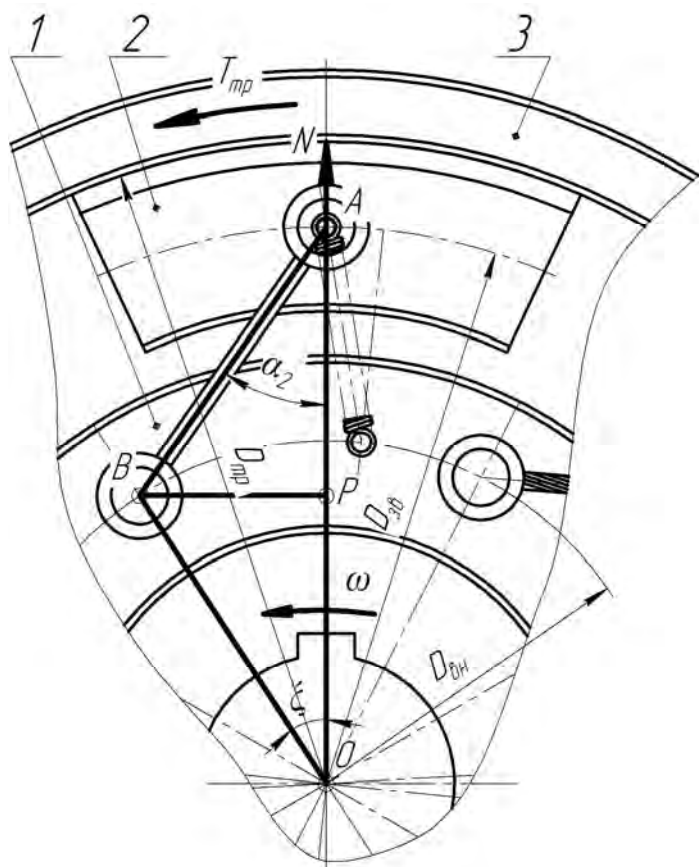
Розрахункова схема фрикційної колодкової муфти з циліндричними поверхнями тертя та канатними елементами
